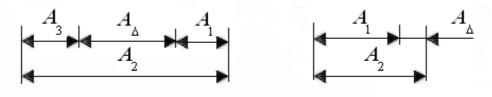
Схемы размерных цепей вала и узла конструкции
